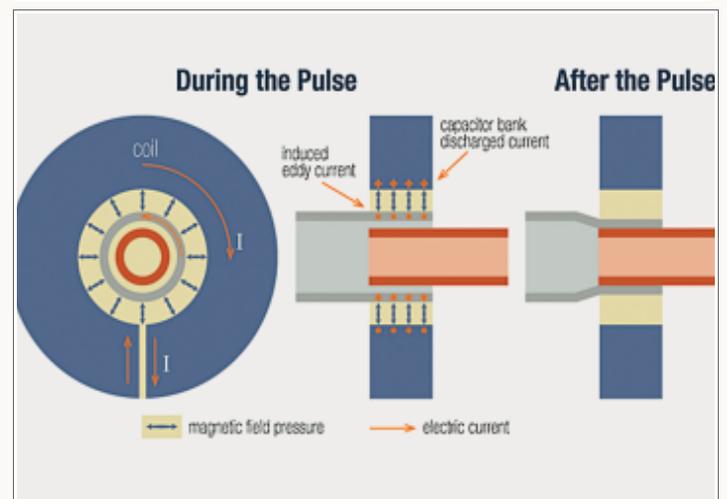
principe du soudage par impulsion magnétique de produits tubulaires
